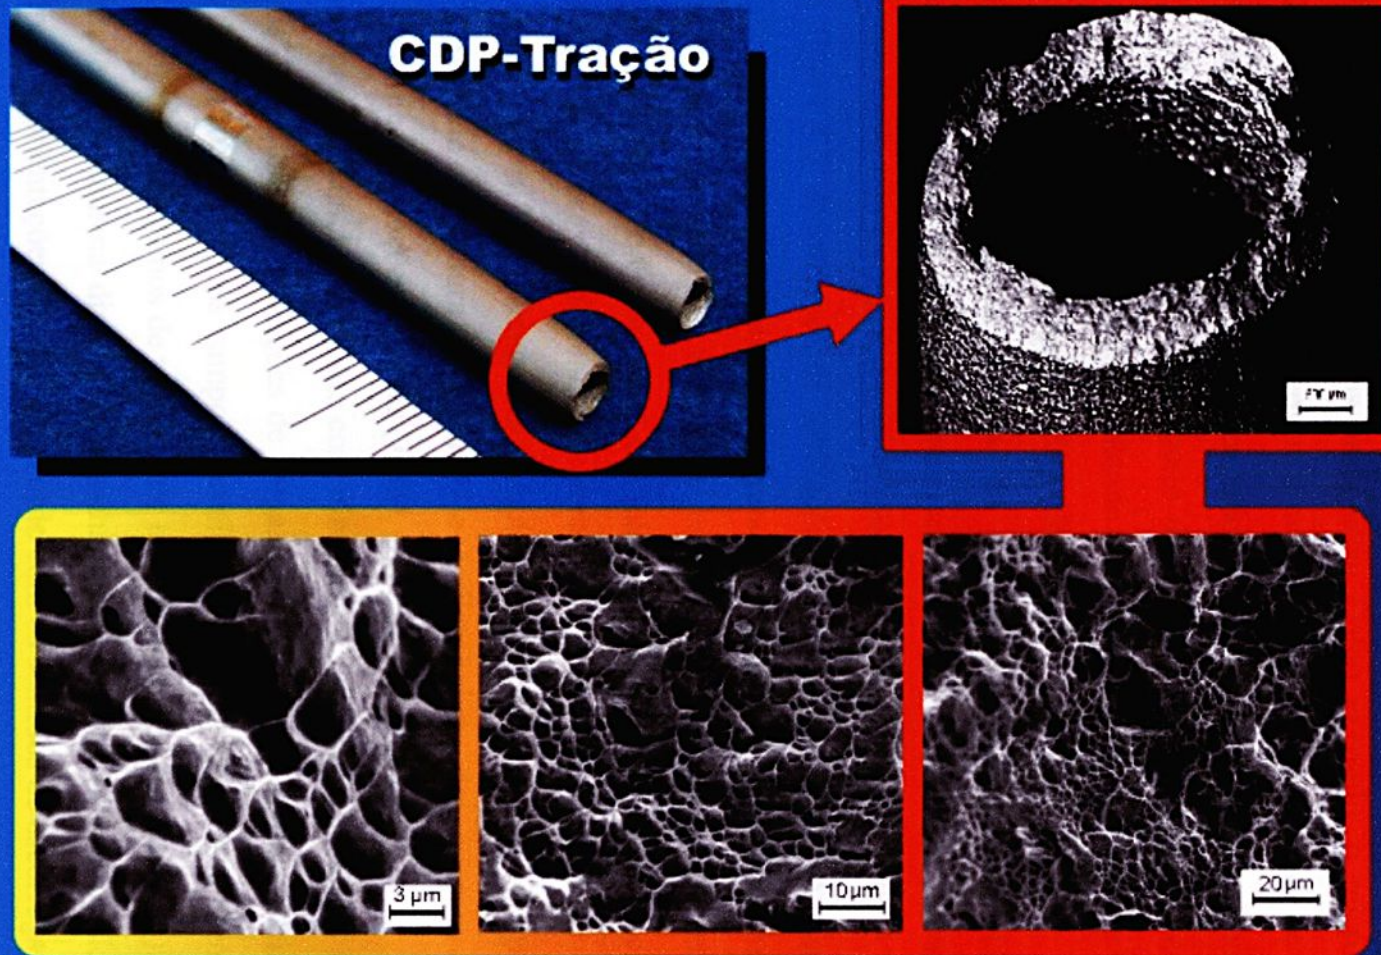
Análise da superfície de fratura de um corpo-de-prova soldado (#A)
